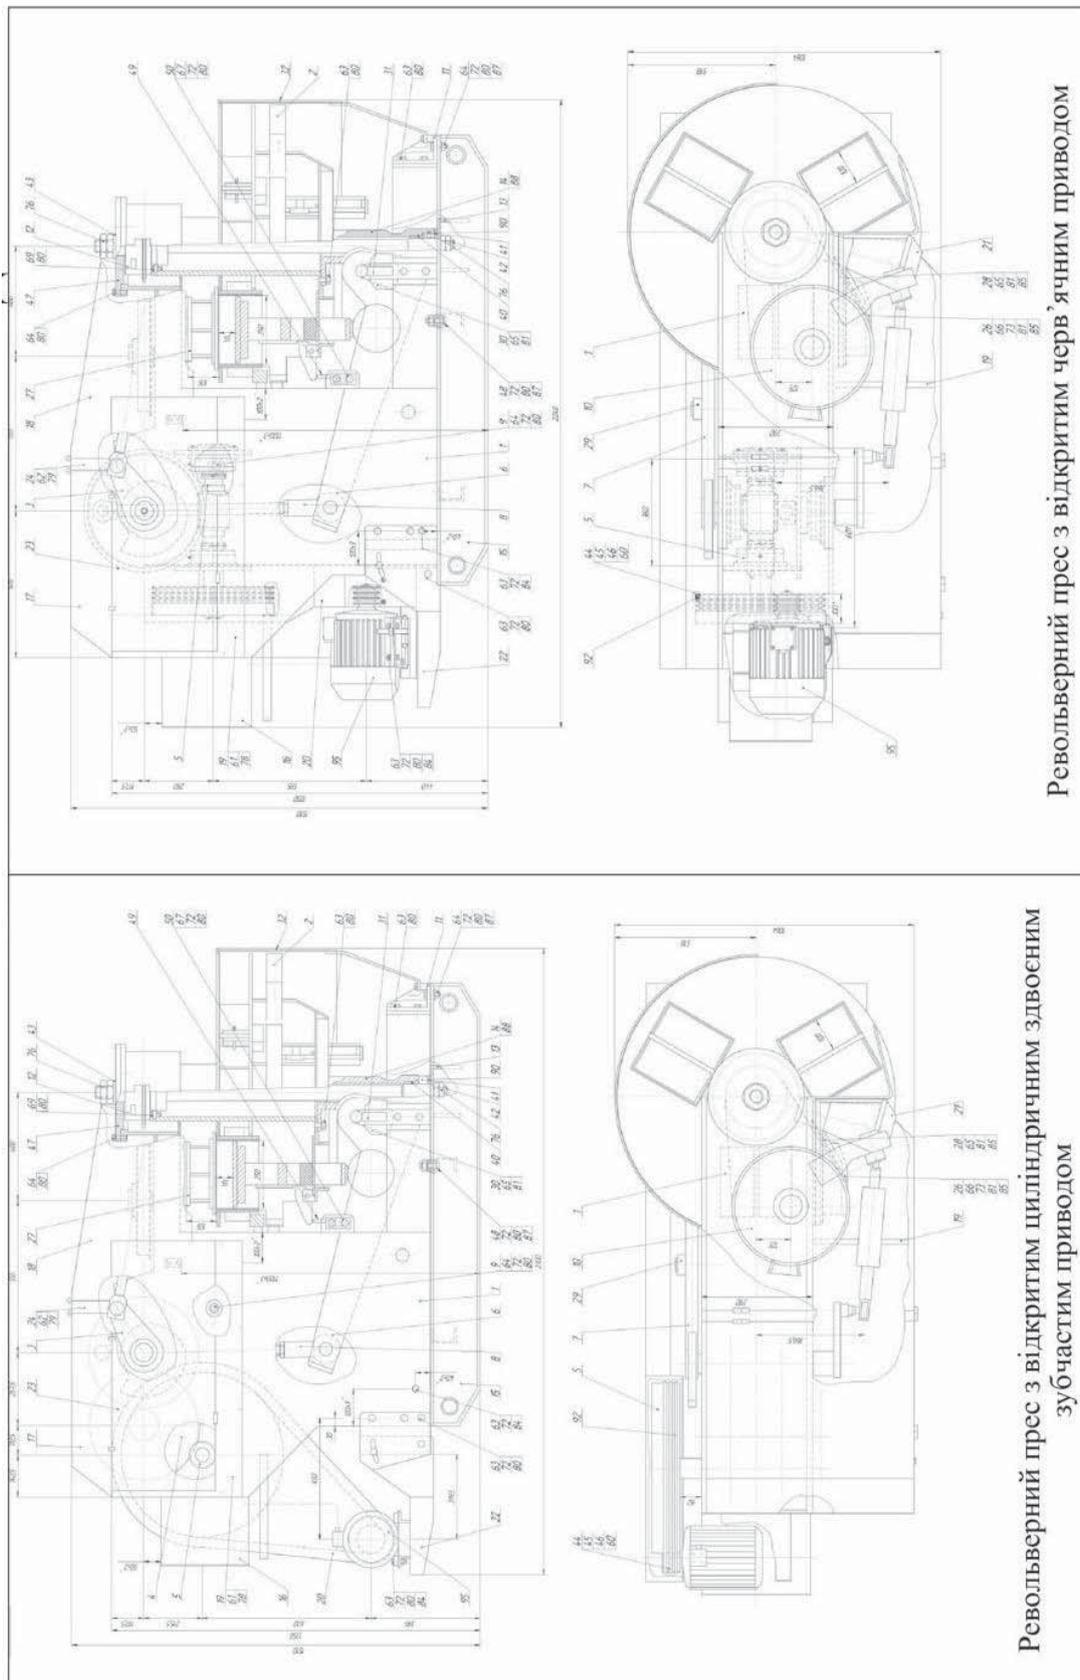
Вид загальний револьверного преса для формування напівфабрикатів керамічної цегли
